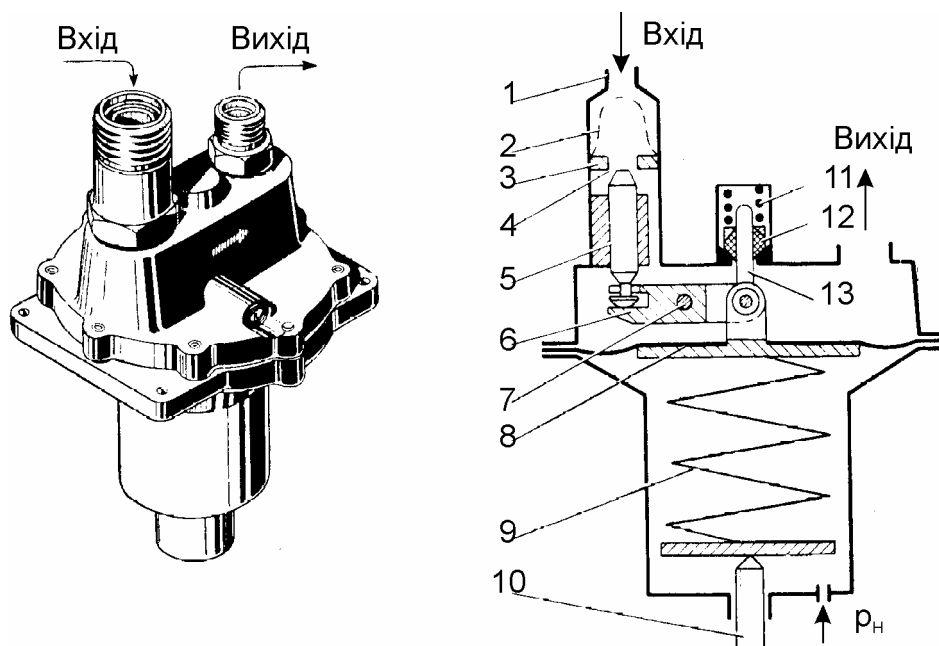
Редуктор 1848ВТ (МиГ-25/29):
